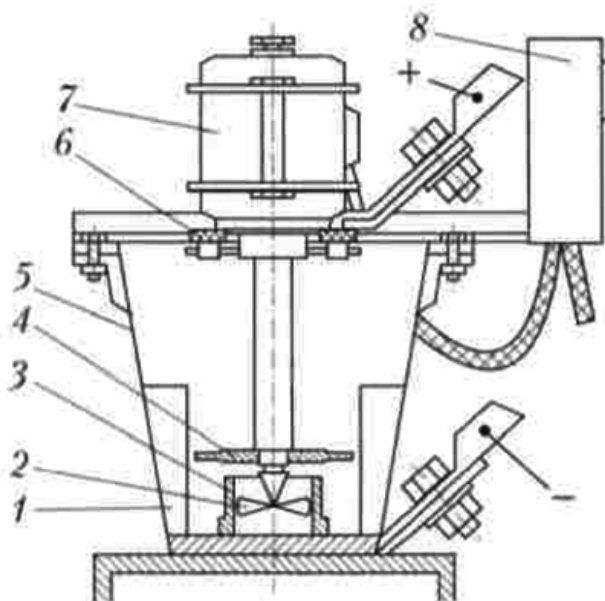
Схема станка для обработки поверхностей электропроводным наполнителем
